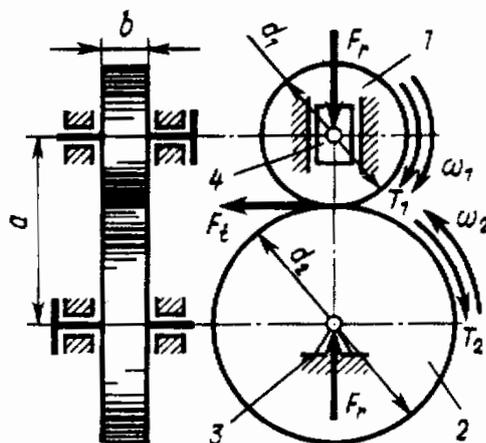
Схема фрикционного механизма: 1- ведущий каток; 2 – ведомый каток; 3 – неподвижная опора; 4 – подвижная опора
